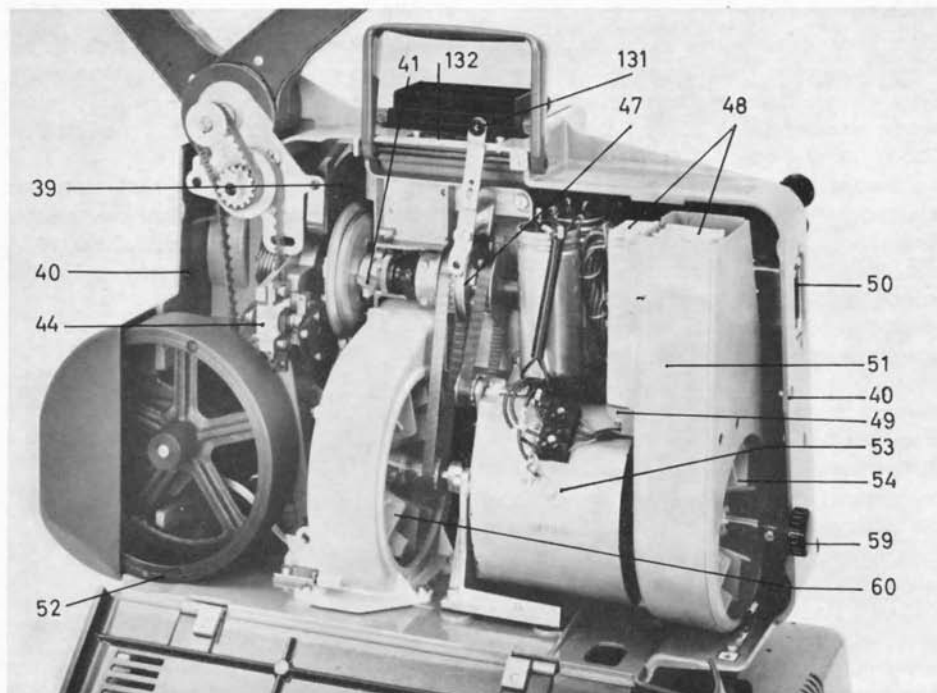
Innenansicht des BAUER-P 5-Tonprojektors. Gehäusedeckel offen.
